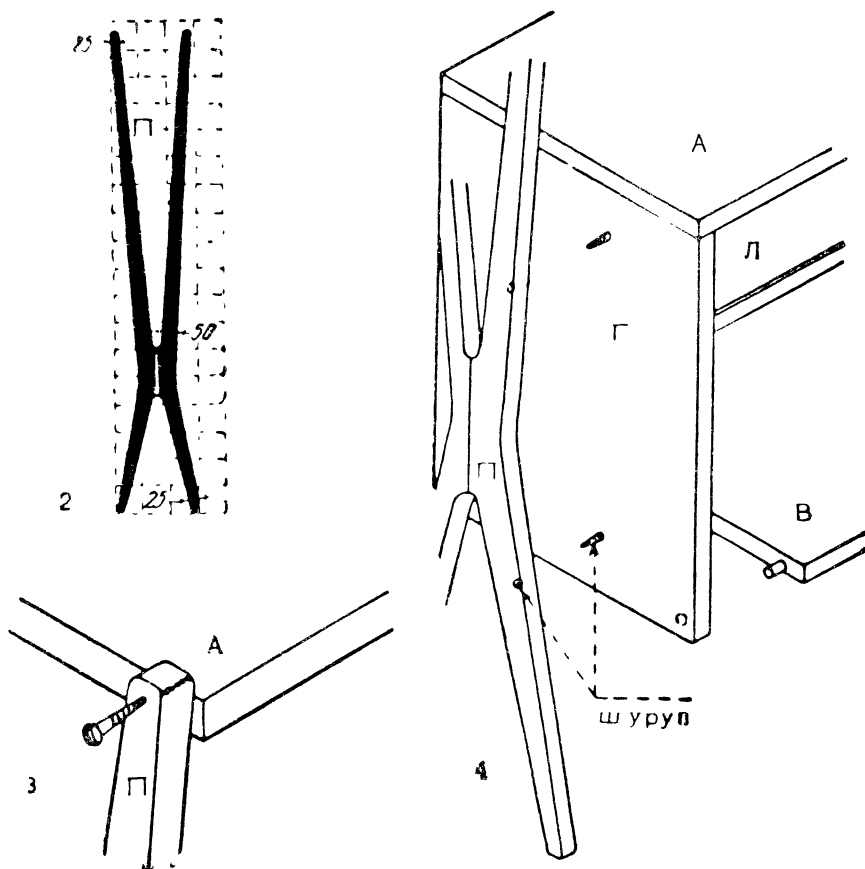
4. 2 — шаблон для изготовления ножек (размер клетки — 100 мм); 3 — эскиз соединения полки с ножкой; 4 — эскиз соединения стенки с ножками и нижним полком.
